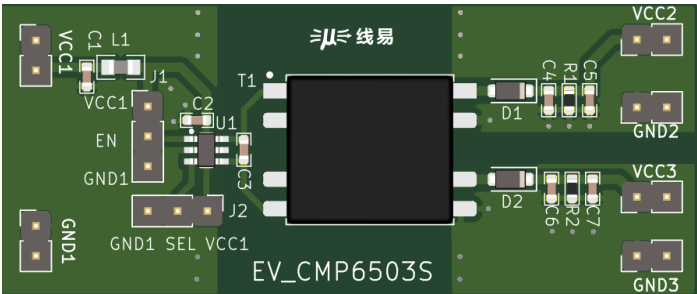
PCB 示意图(尺寸: 25 x 60mm)
